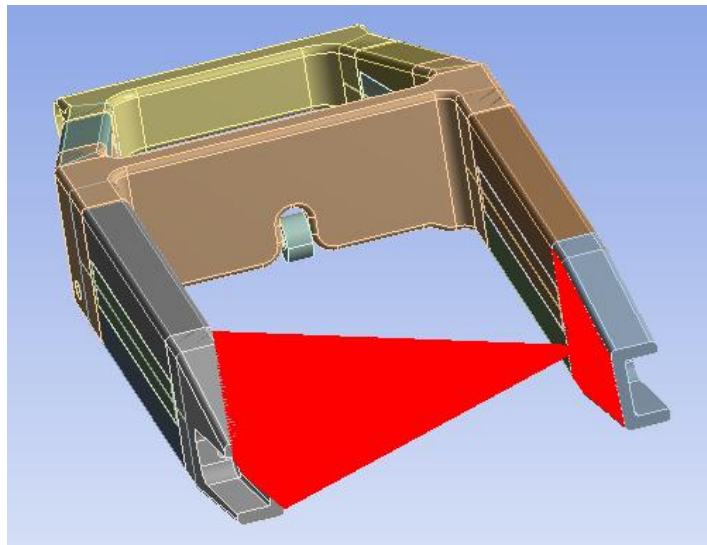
Detalle conexión rígida entre anclajes de neumático.
